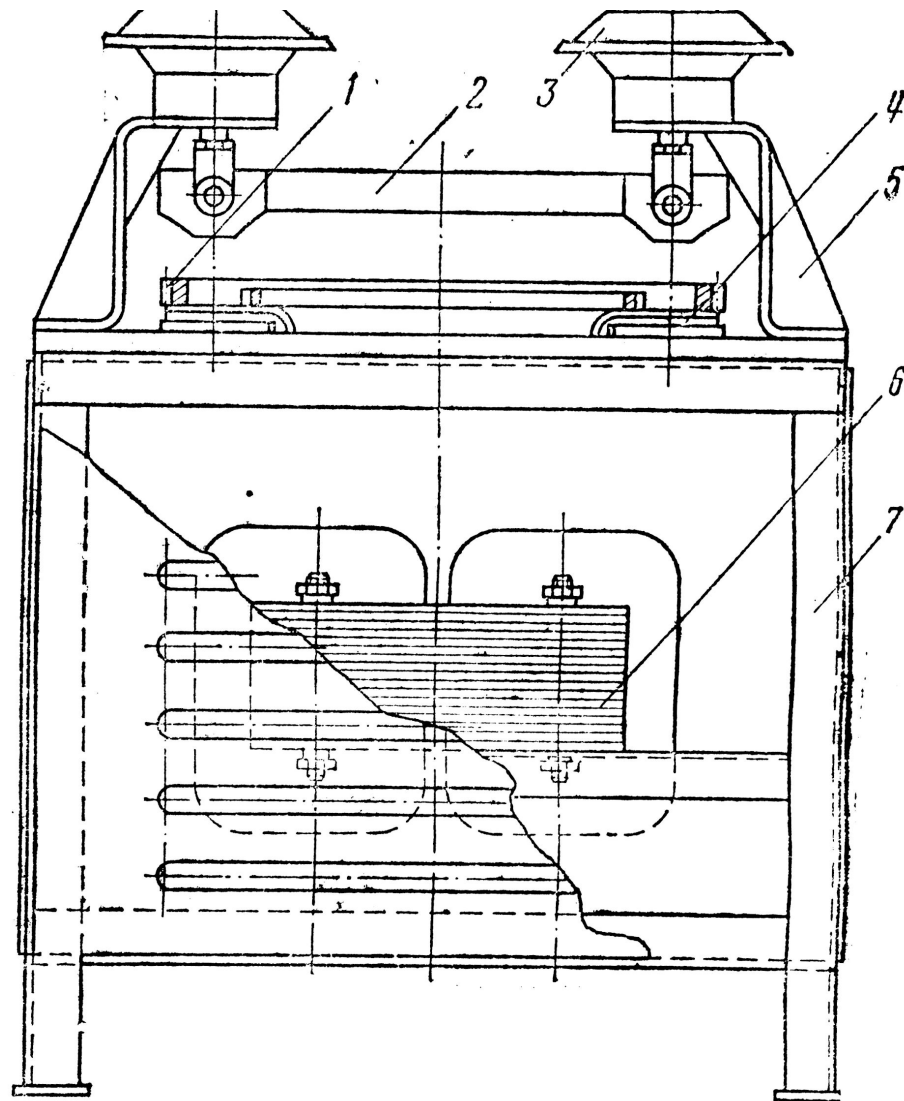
Приспособление для нагрева зубчатого венца перед установкой на маховик
